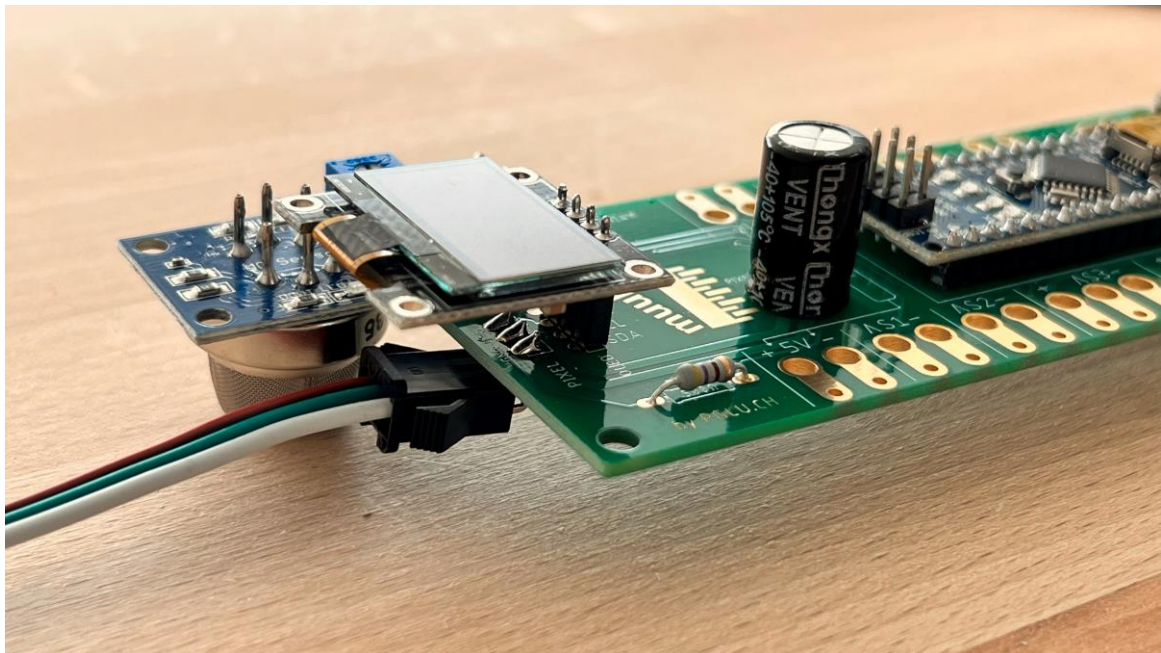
Stripe einstecken. Auf Kabelfarben achten: gleich wie hier auf dem Bild!
